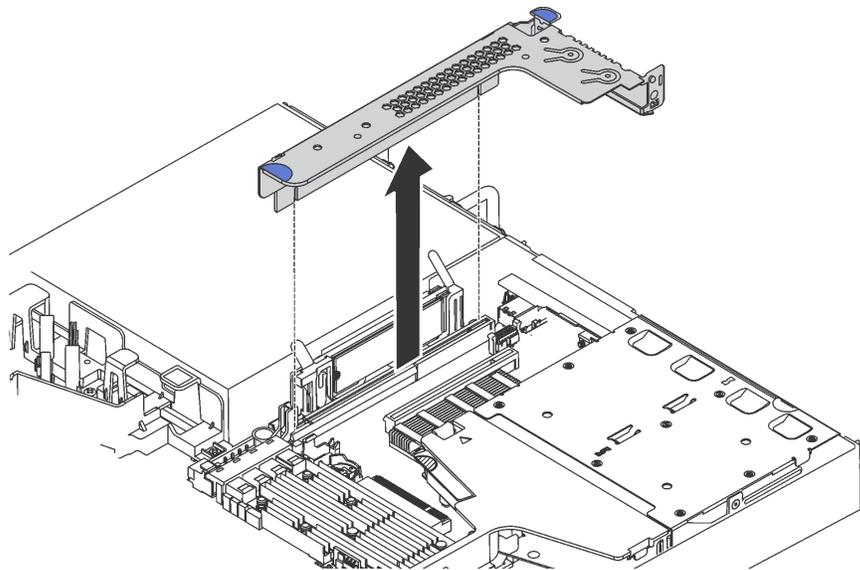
Entfernen der Adapterkartenbaugruppe
